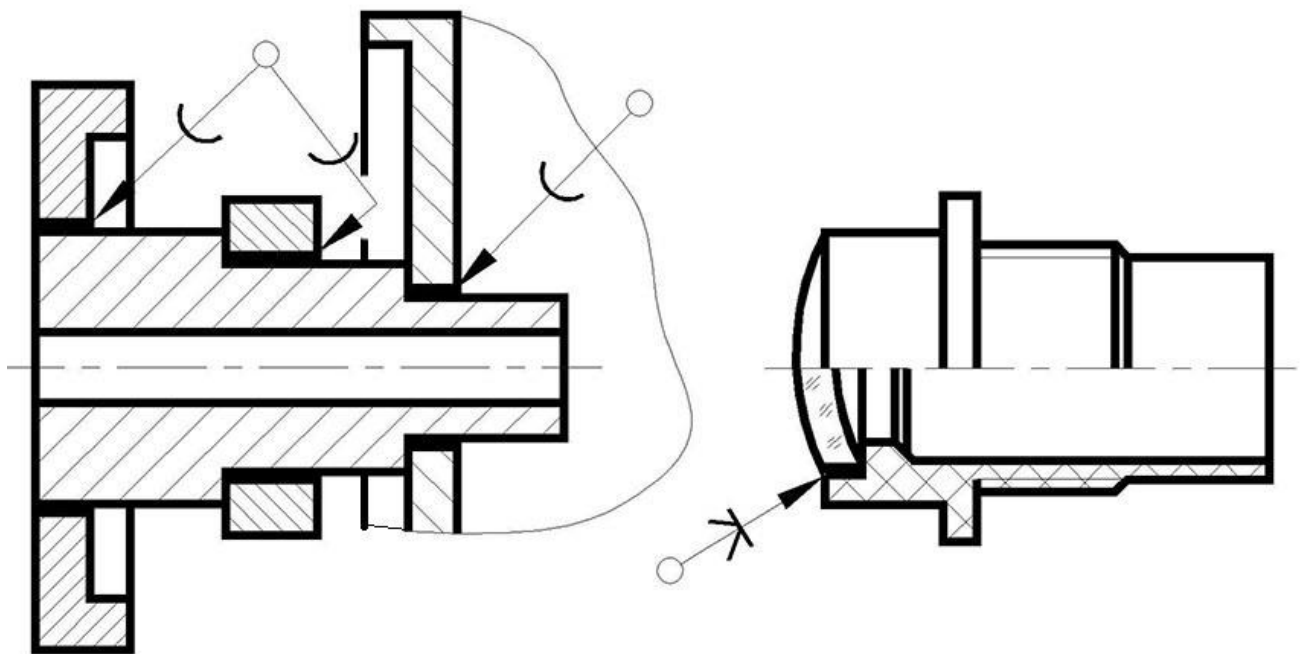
Зразок кресленика паяного та клеєного з'єднання.
